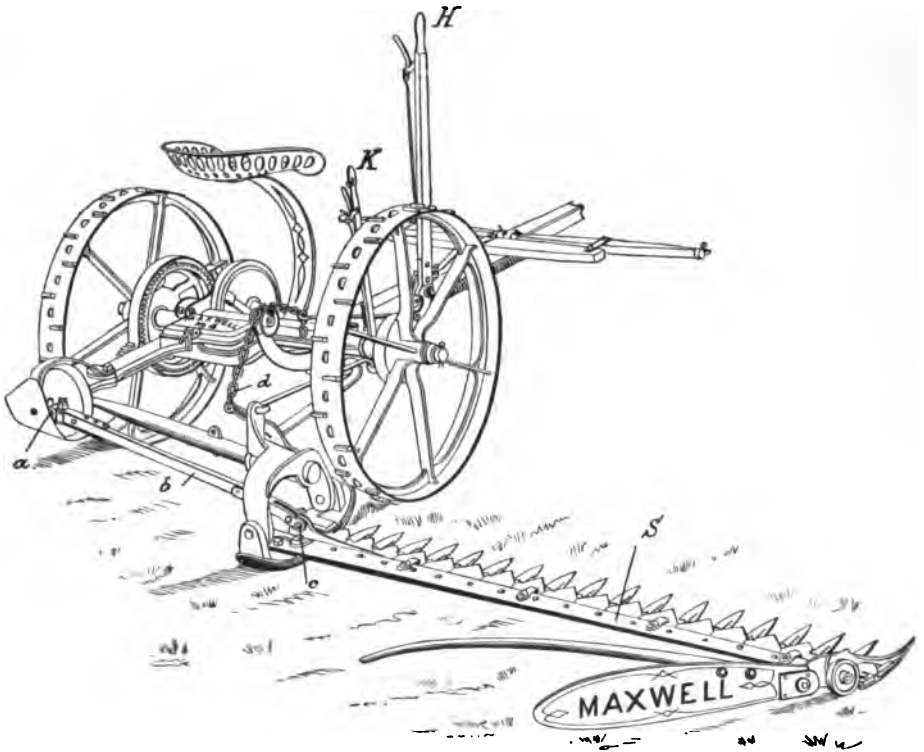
Grasmähmaschine mit Hinterschnitt, von hinten gesehen.
